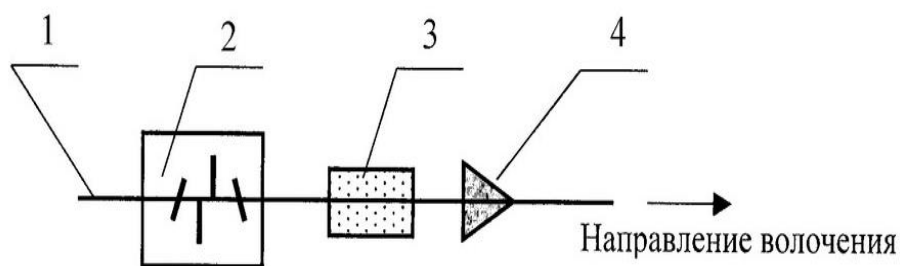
Схема для очистки поверхности горячекатаного проката:
